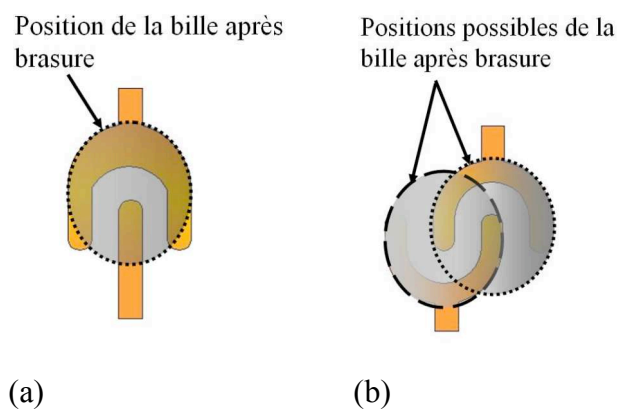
Positions occupées par la bille après soudure pour la géométrie C (a) et D (b).
